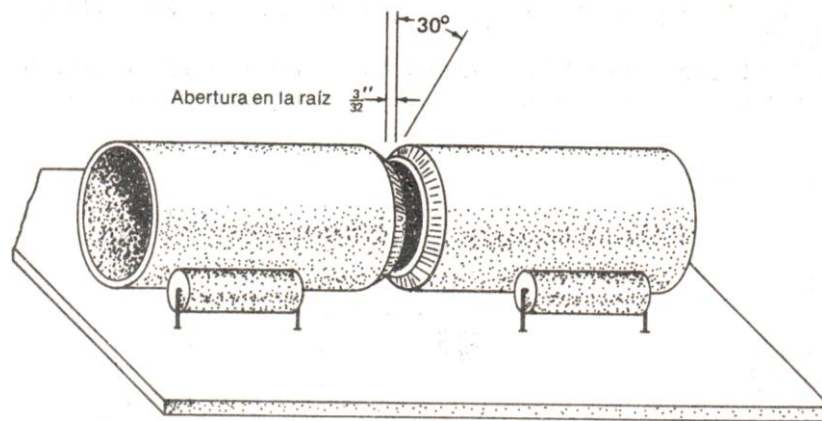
Colocación de los dos extremos de los tubos a soldar.
